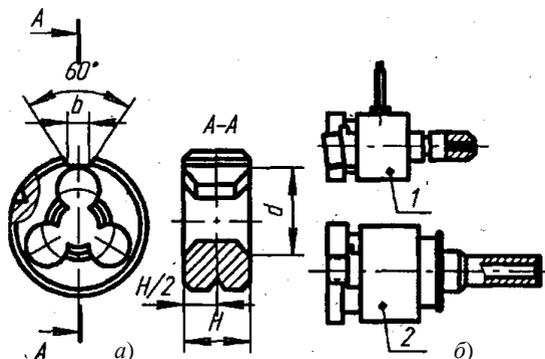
Пример инструментов для нарезания резьбы: а – плашка; б – самораскрывающаяся резьбовая головка
